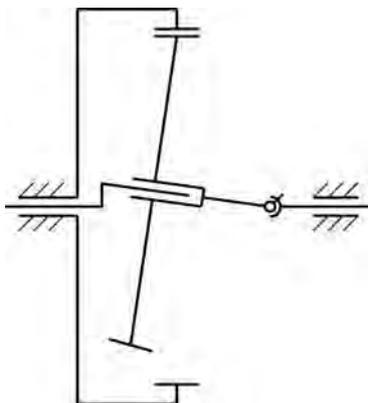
Кинематическая схема прецессионной передачи типа К-Н-V
